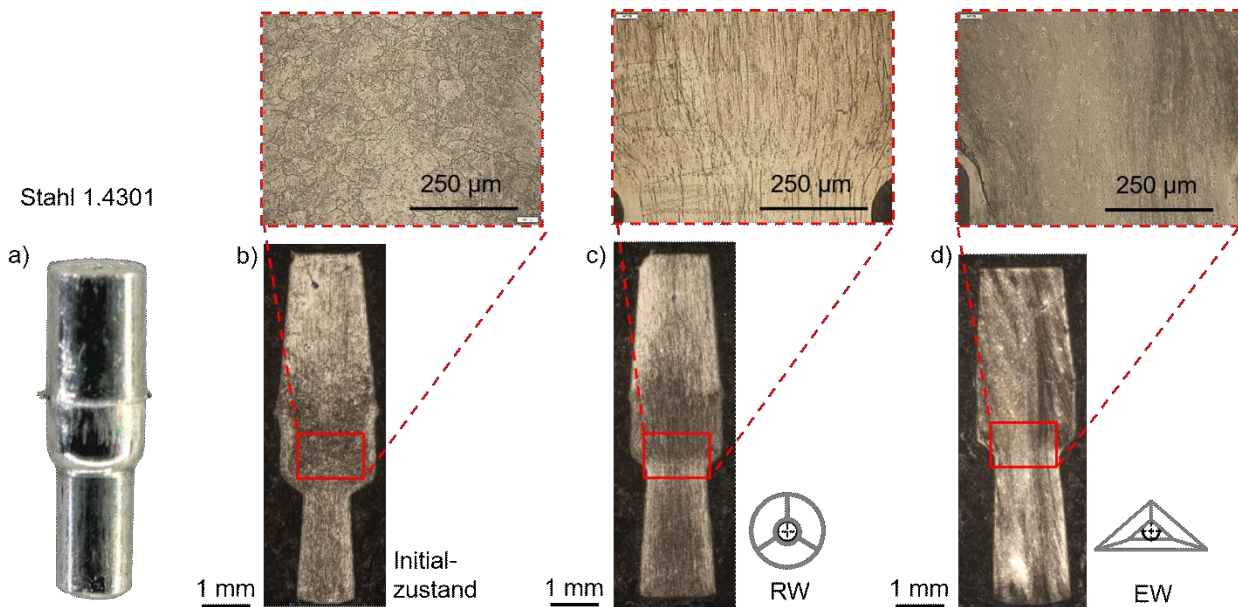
Fließgepresste Bauteile a) Bauteil nach dem Fließpressen; Mikrostruktur b) ohne Konditionierung; nach dem Rundkneten mit c) Rundwerkzeugen; d) exzentrischen Werkzeugen.
